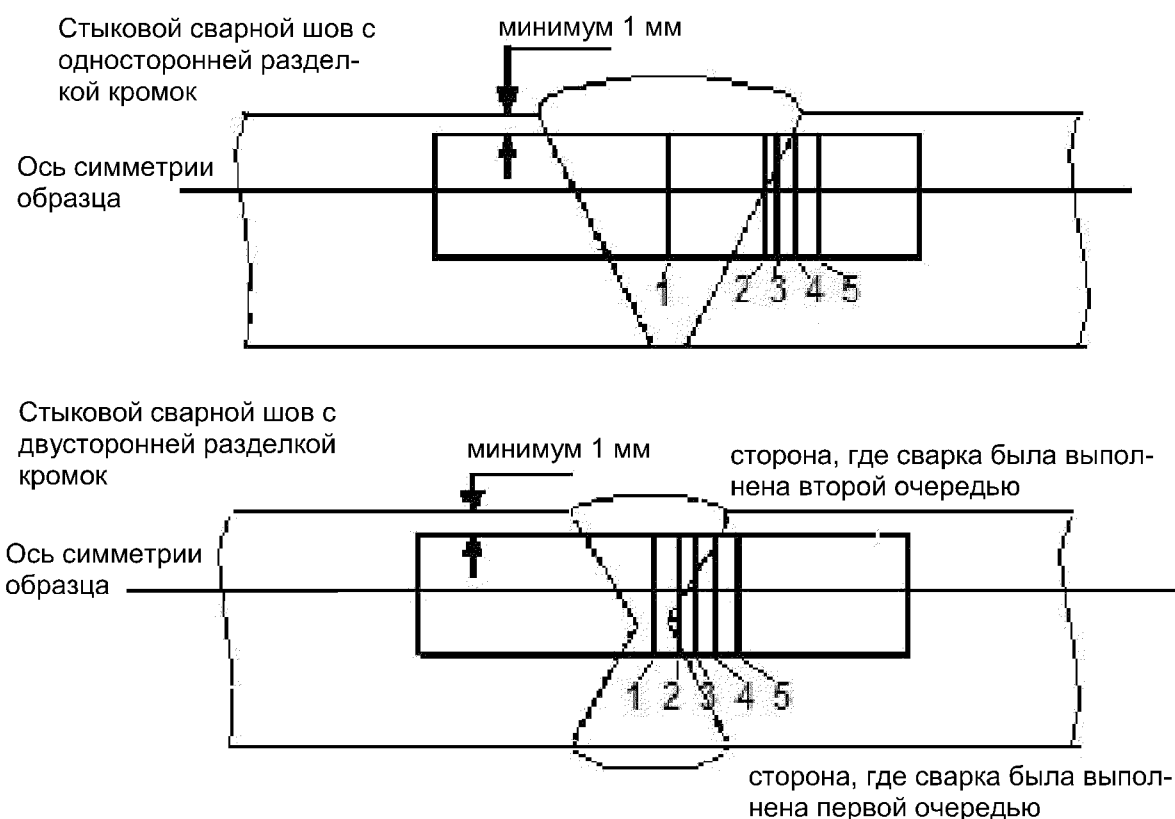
Положение испытательного образца из наплавляемого металла
